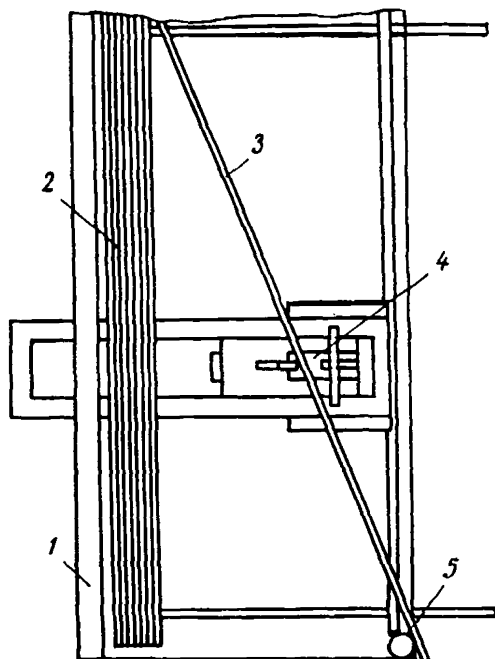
Рис. II. Отбор стержней из пакета с помощью подвижного механизма захвата и ролика
